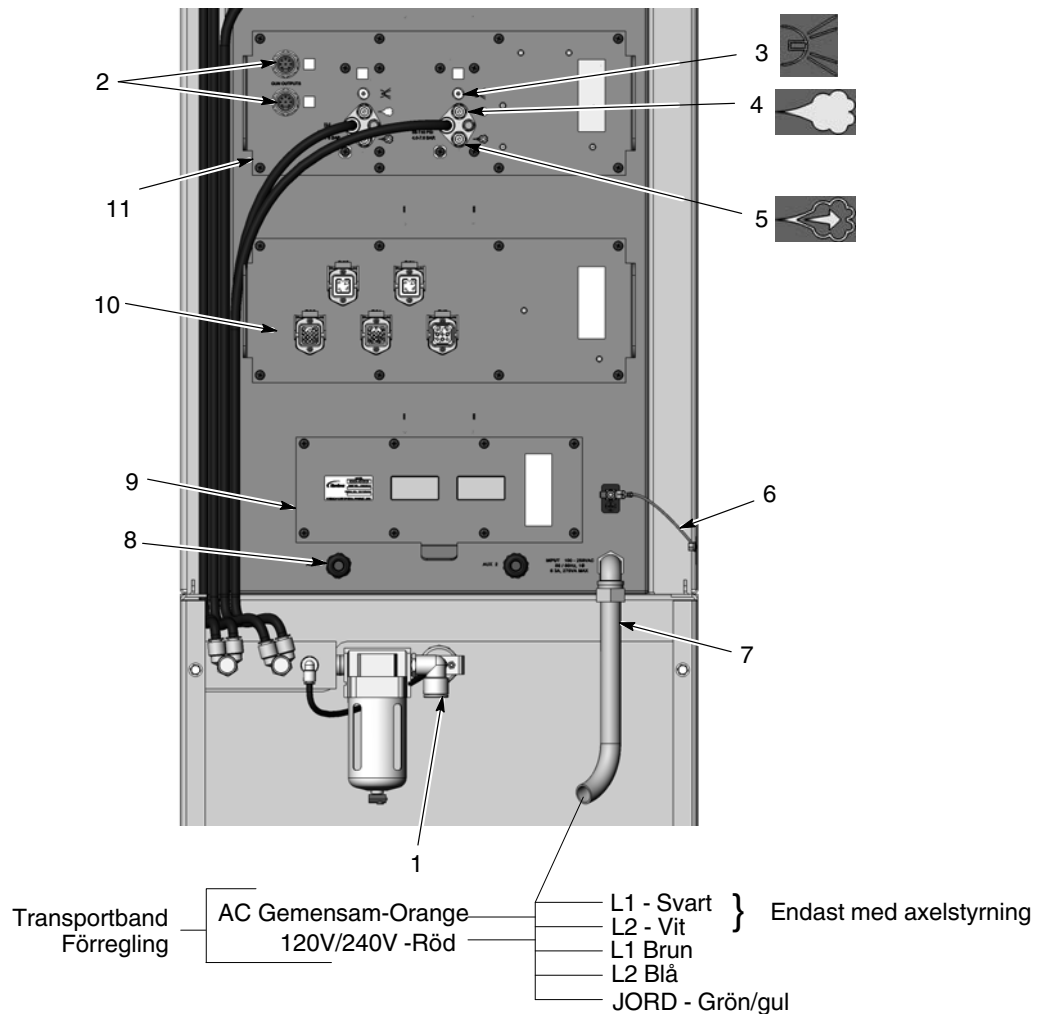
Flerpistols styrenhet - matningsspänning-, luft-, pistolanslutningar (bakre panel och sockelpanel avtagna)
